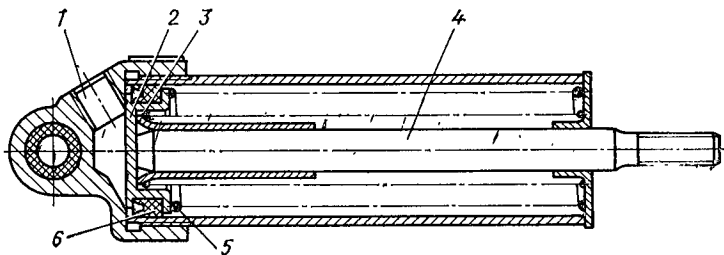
Пневмоцилиндр привода заслонки механизма вспомогательного тормоза;
